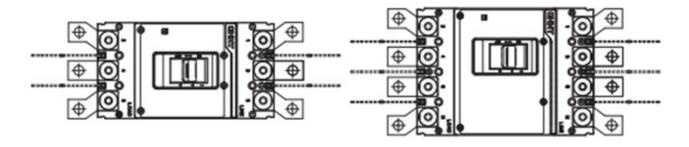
Схема установки соединительной пластины NXM(S)-400, 630, 800, 1000
